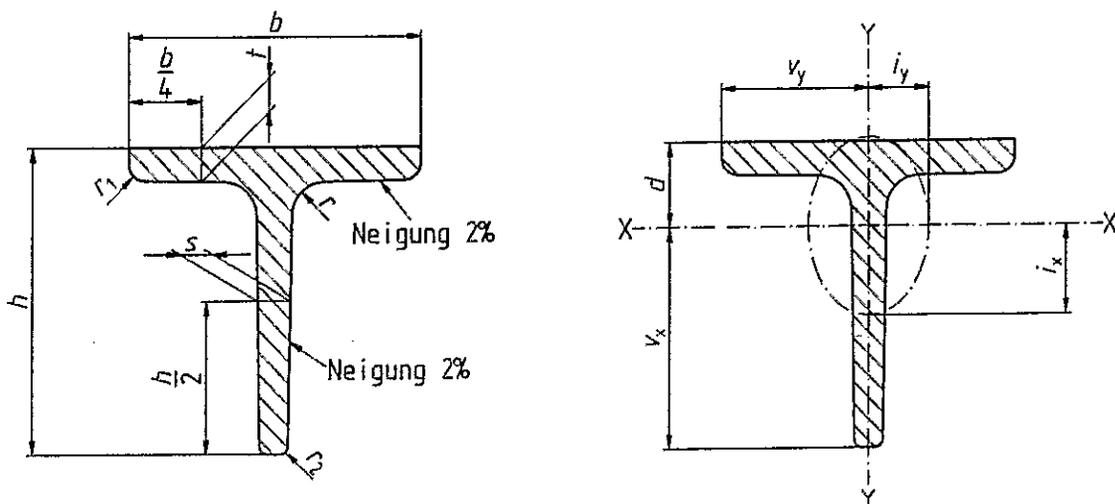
Warmgewalzter gleichschenkliger T-Stahl mit gerundeten Kanten und Übergängen
